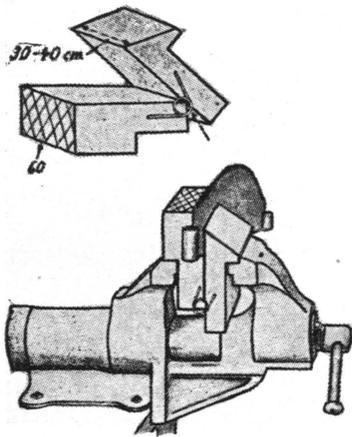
Schraubstock mit hölzernen Klemmbacken als Einspannvorrichtung. (Aus Gläser u. Steitzel: Die Pflege der Waldsäge.)
